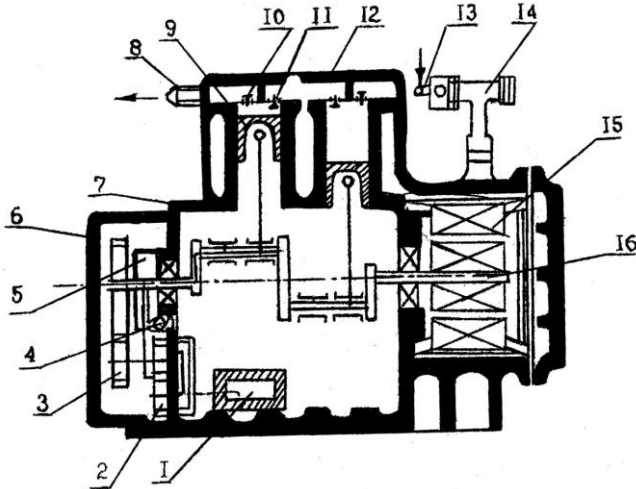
Схема компресора 2ФУБC9: 1 - фільтр масляний; 2 - насос масляний; 3 - шестерні; 4 - клапан перепускний; 5 - підшипник фальшивий; 6 - кришка; 7 - блок-картер; 8 - вентиль нагнітальний; 9 - шатунно-поршнева група; 10 - нагнітальні клапани; 11 - усмоктувальні клапани; 12 - кришка циліндрів; 13 - вентиль усмоктувальний; 14 - фільтр газовий; 15 - електродвигун; 16 - вал колінчастий.
